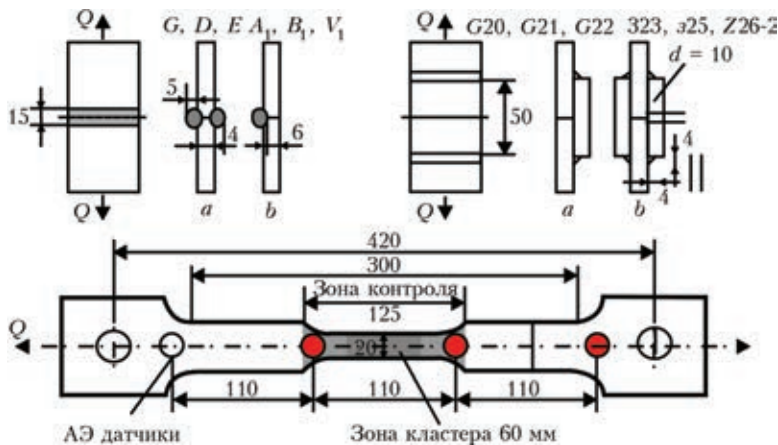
Образцы для исследования влияния сварки и видов сварных соединений на акустические характеристики материалов. Материал соединения – сталь 17ГС; $\delta = 8$; сварка ручная; режим сварки $I = 210 \dots 220$ А; электрод УОНИ-13/45
